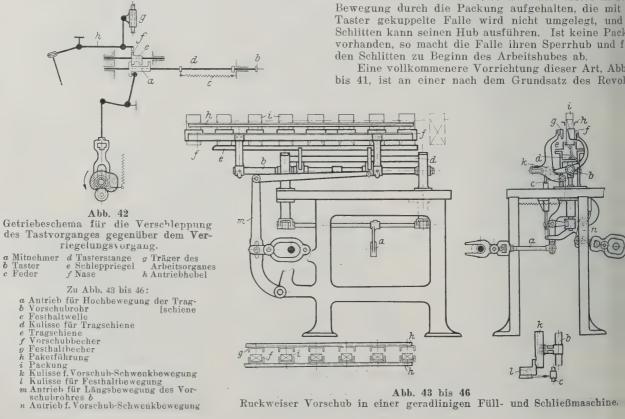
bis 46 Ruckweiser Vorschub in einer geradlinigen Füll- und Schließmaschine.
